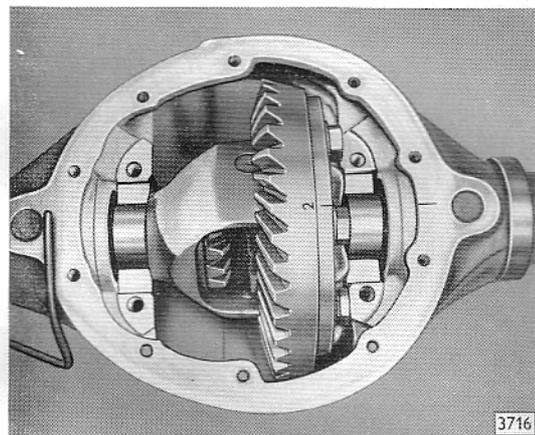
Lage des Ausgleichgehäuses zum Hinterachsgehäuse gezeichnet
